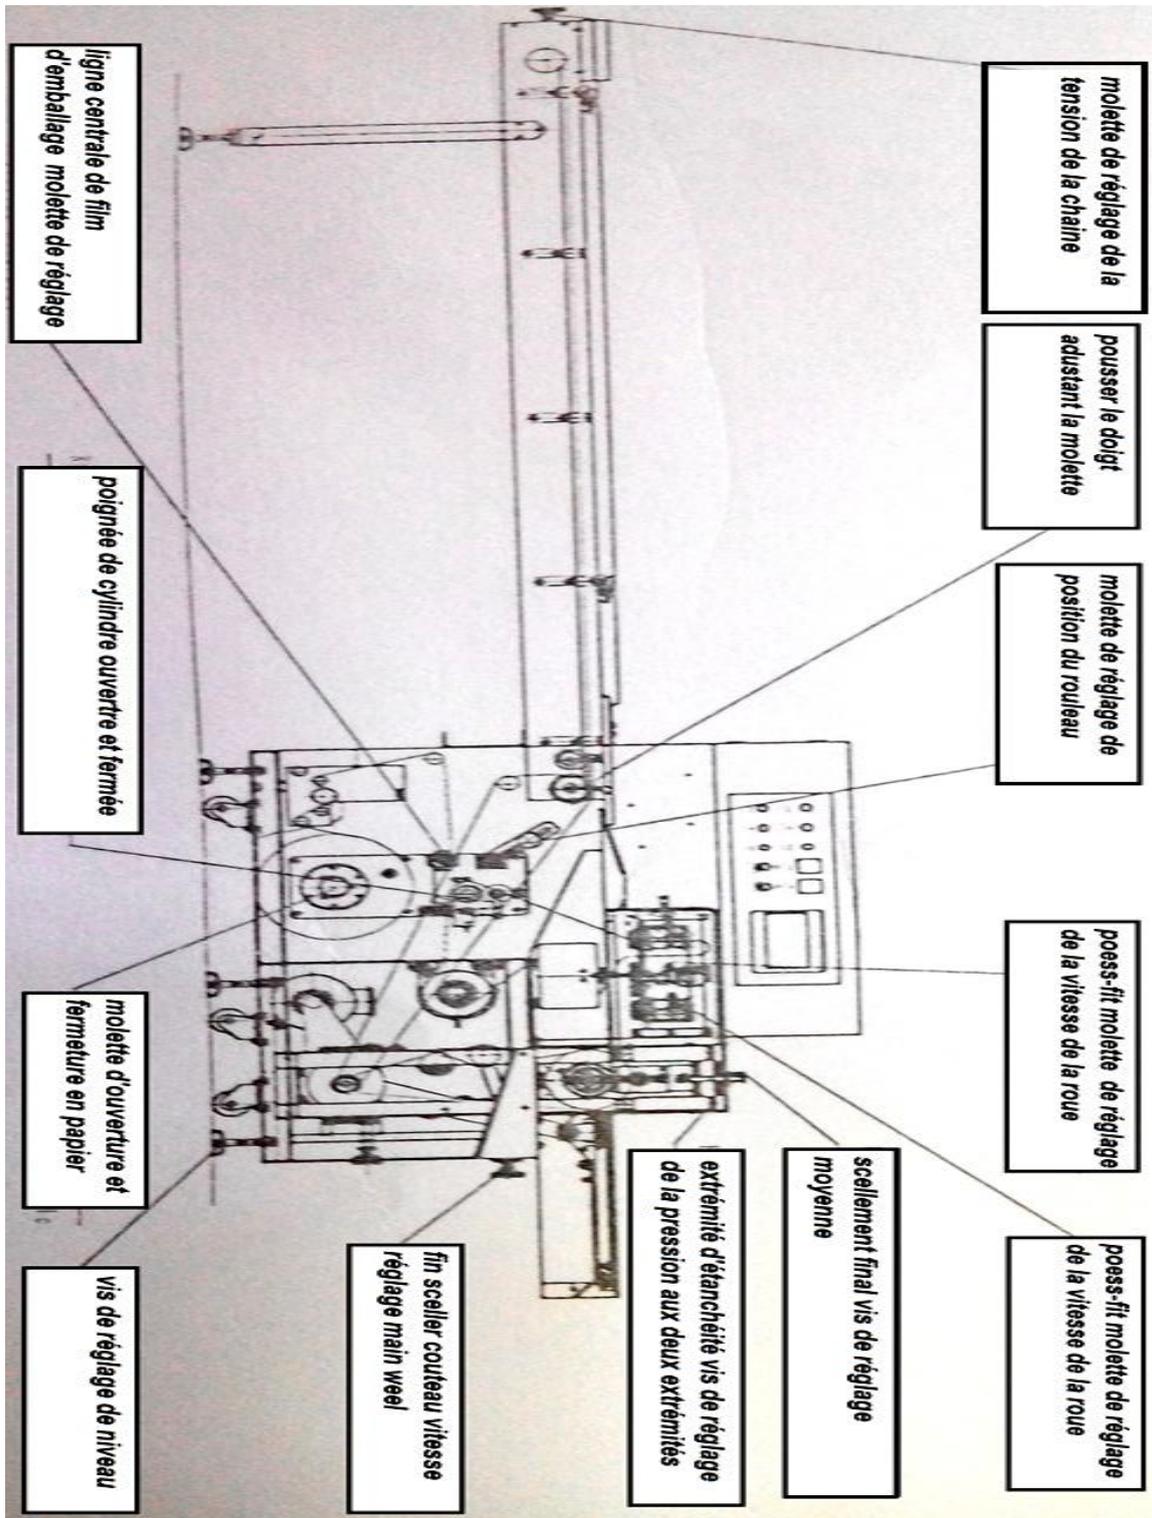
Positions et noms des composants de réglage de la machine [3].
